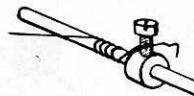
zeigt die Befestigung einer Schnur auf einer Achse mit einem Stellring usw.
